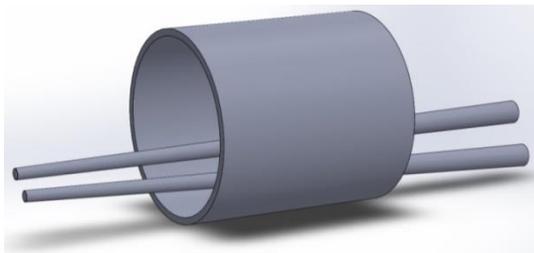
Два длинномера в корпусе корообдирочного барабана
